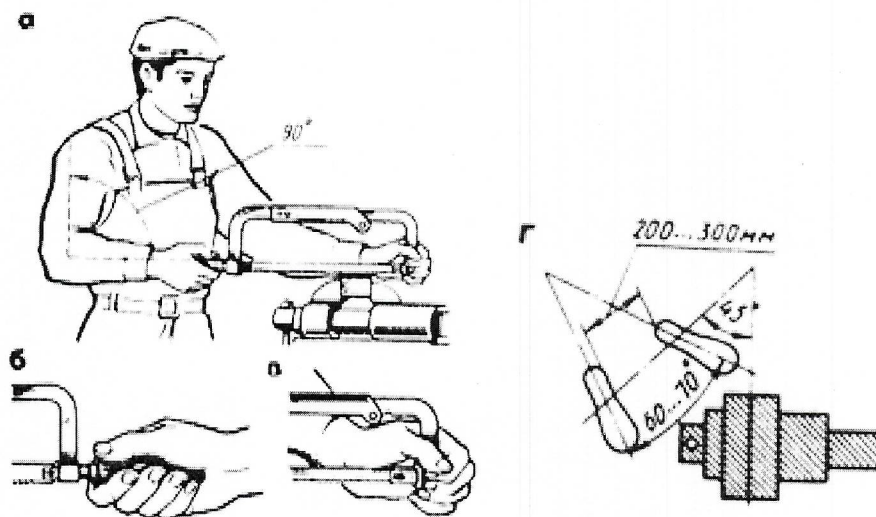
Положение при работе: а – корпуса и ножовки, б, в – соответственно правой и левой рук, г – ног
